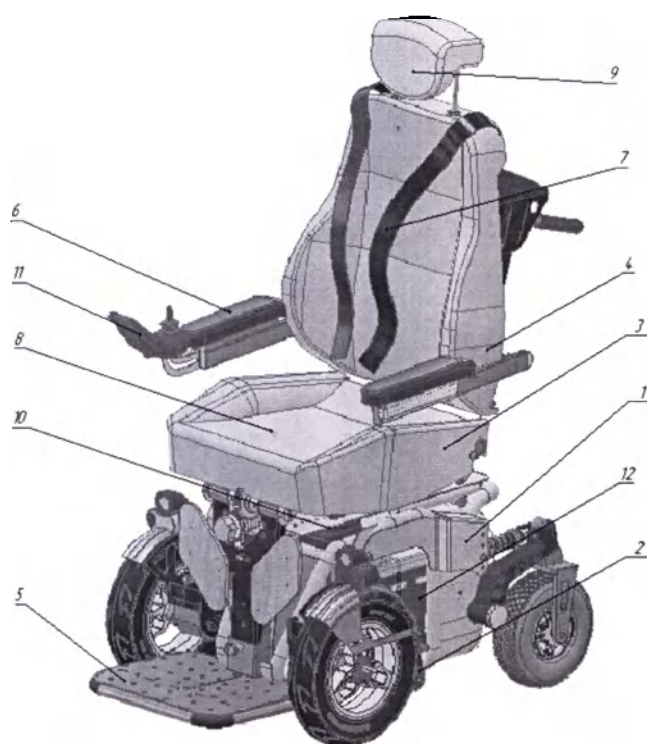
Внешний вид кресла-коляски «Гефест Б»
